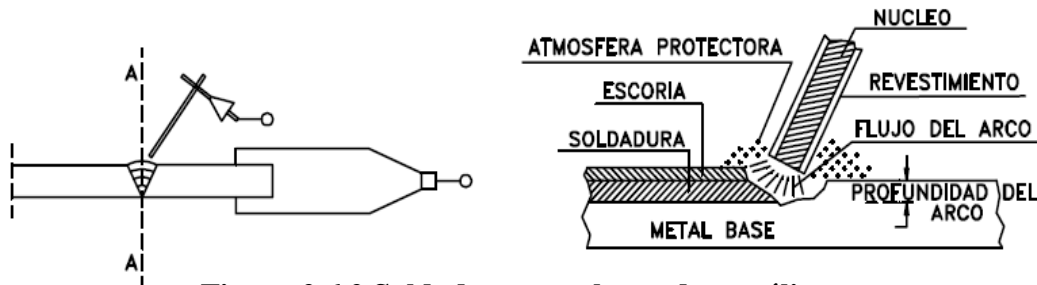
Soldadura con electrodo metálico
